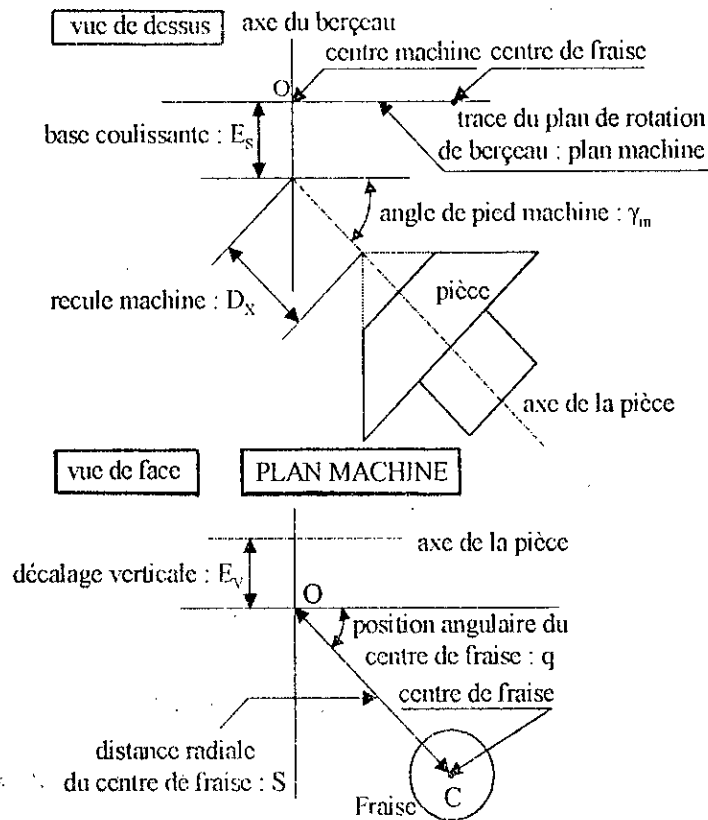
Définition des différents réglages machine pour le positionnement de la pièce [65].
